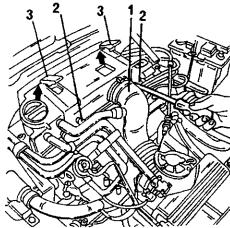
При снятии головки цилиндров двигателя тила XU сначала снять указанные детали, чтобы обеспечить доступ к воздушному фильтру на крышке головки цилиндров.
